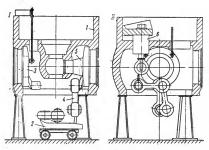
Сборка механизмов поворога бескрестовинного рабочего колеса.
